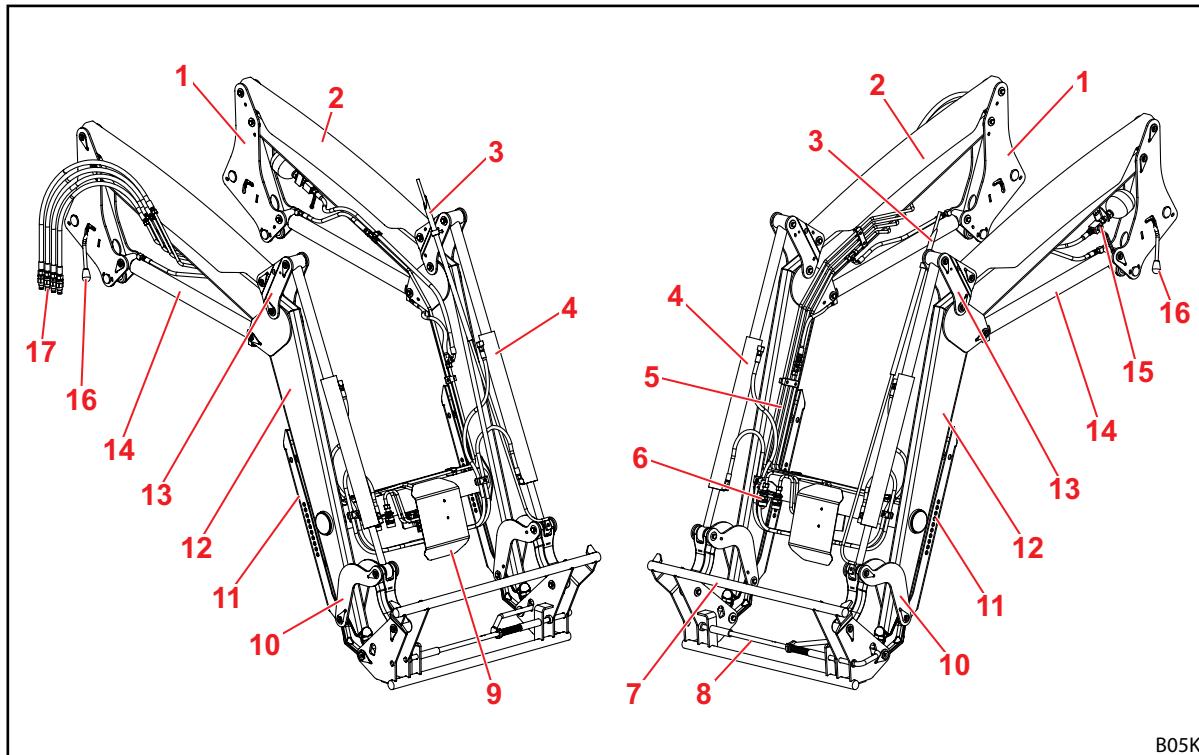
Frontlader P (mit mechanischer Parallelführung)
